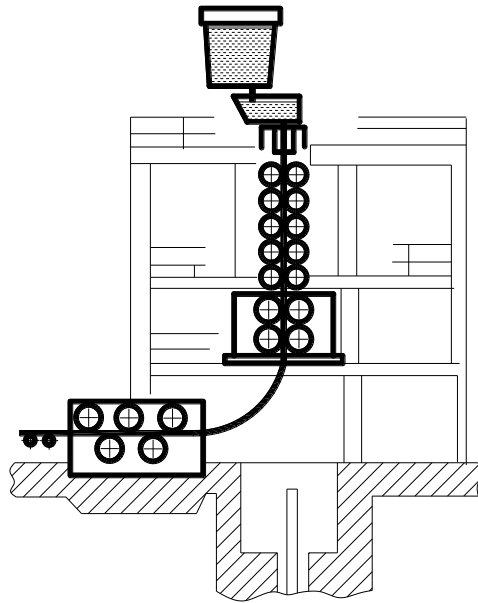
Схема вертикальної МБЛЗ з вигином заготовки
